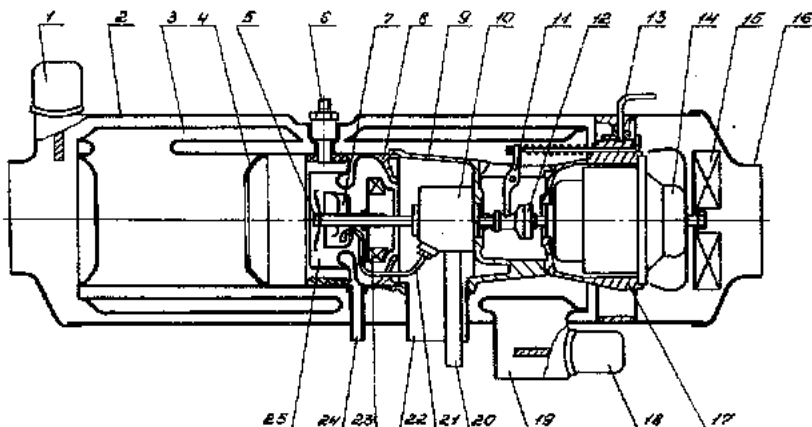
Отопительно-вентиляционная установка типа ОВ-65:
